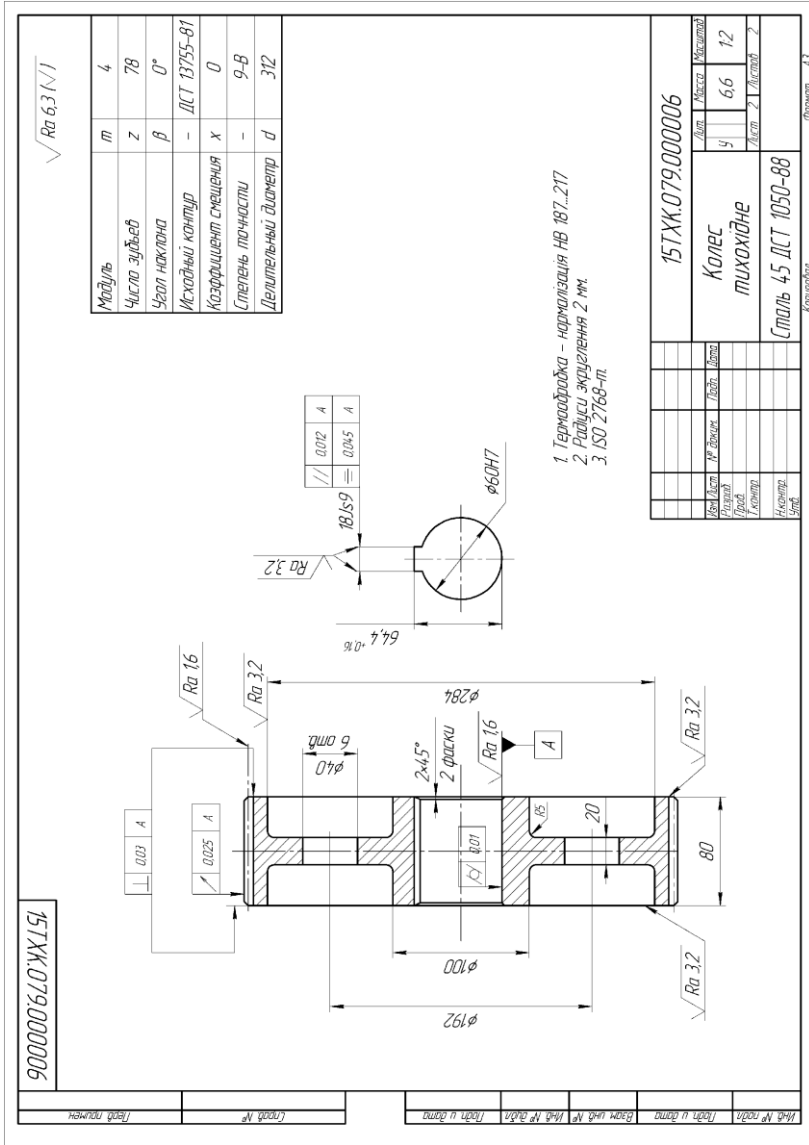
Приклад виконання робочого креслення зубчастого колеса
